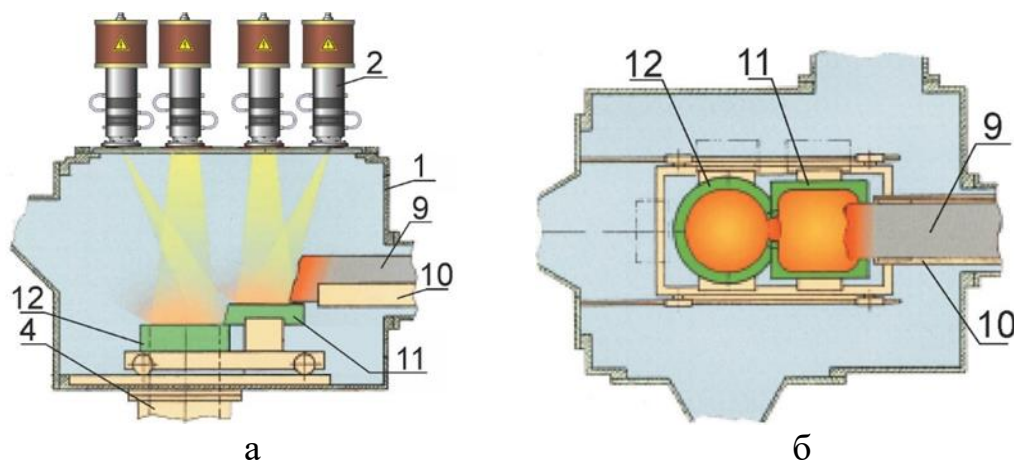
Схема робочої камери: вид спереду (а); вид зверху (б): (1 - робоча камера; 2 - електронні гармати; 4 - механізм витягування зливка; 9 - матеріал, що переплавляється; 10 - висувний лоток; 11 - проміжна ємність; 12 – кристалізатор)
